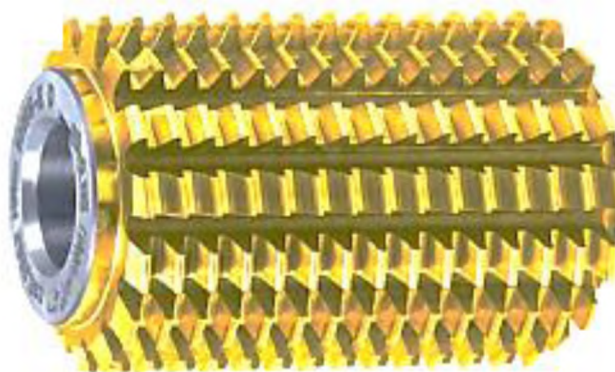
Черв'ячна твердосплавна фреза [3, с.115]
